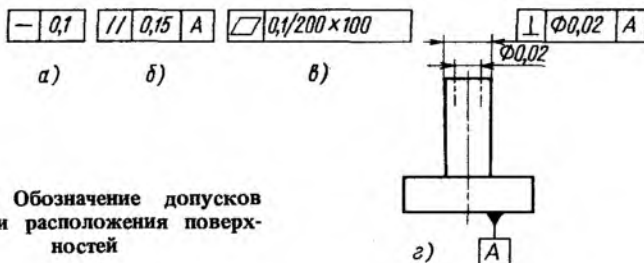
Обозначение допусков формы и расположения поверхностей
